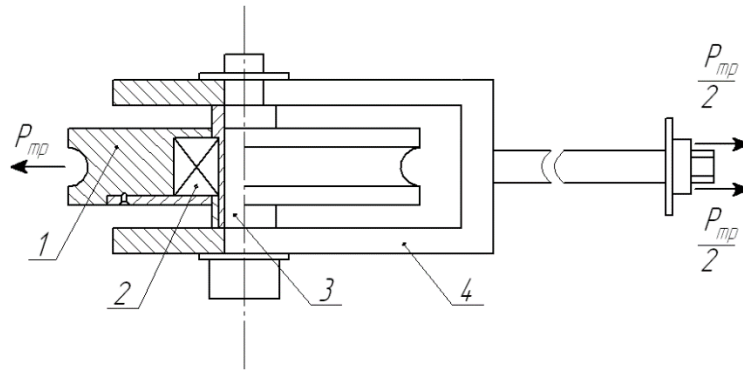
Схема навантаження натяжного пристрою додаткового силового зв'язку: 1 – ролик; 2 – підшипник; 3 – вісь ролика; 4 – вилка ролика.
